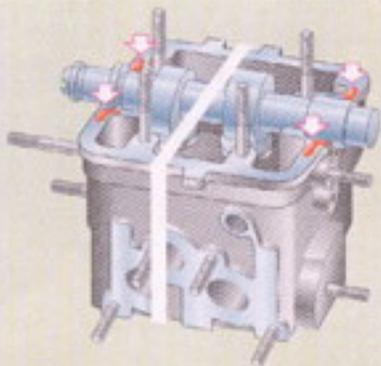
Положение кулачков первого цилиндра при укладке распределительного вала в опоры головки блока цилиндров.
